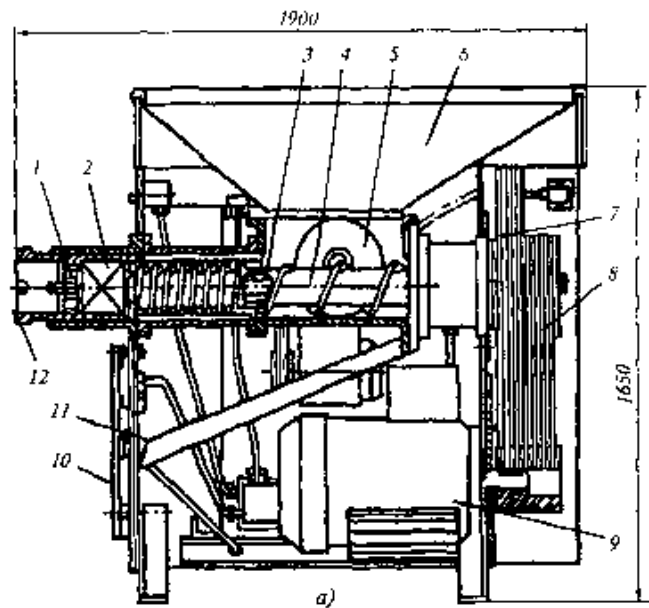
Вовчок К6-ФВП-160: 1 – притискний пристрій; 2 – ріжучий механізм; 3 – ножовий вал; 4 – робочий шнек; 5 – допоміжний шнек; 6 – приймальна чаша; 7,8 – клинописові передачі; 9 – електродвигун; 10 – площадка для санітарної обробки; 11 – жолоб; 12 – гільза.
